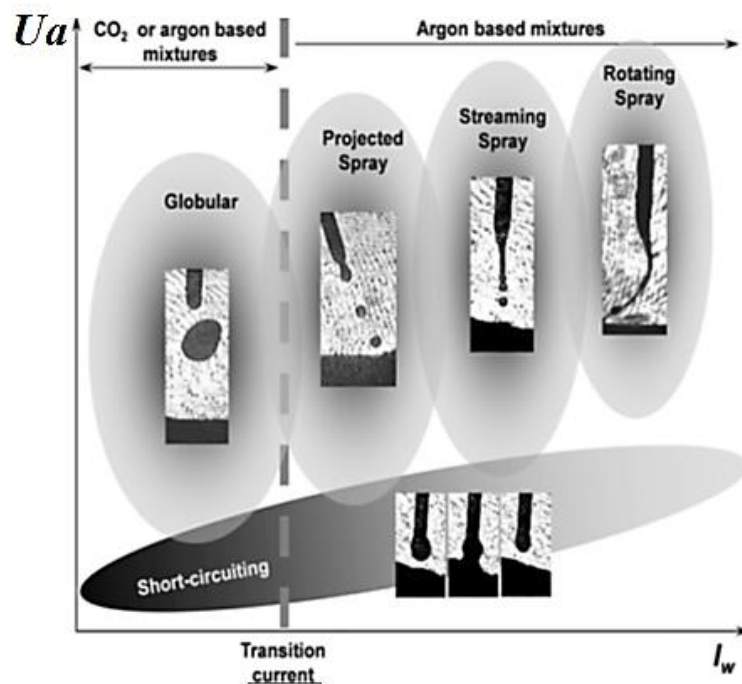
Carte des modes de transfert de métal en soudage MIG [2].
